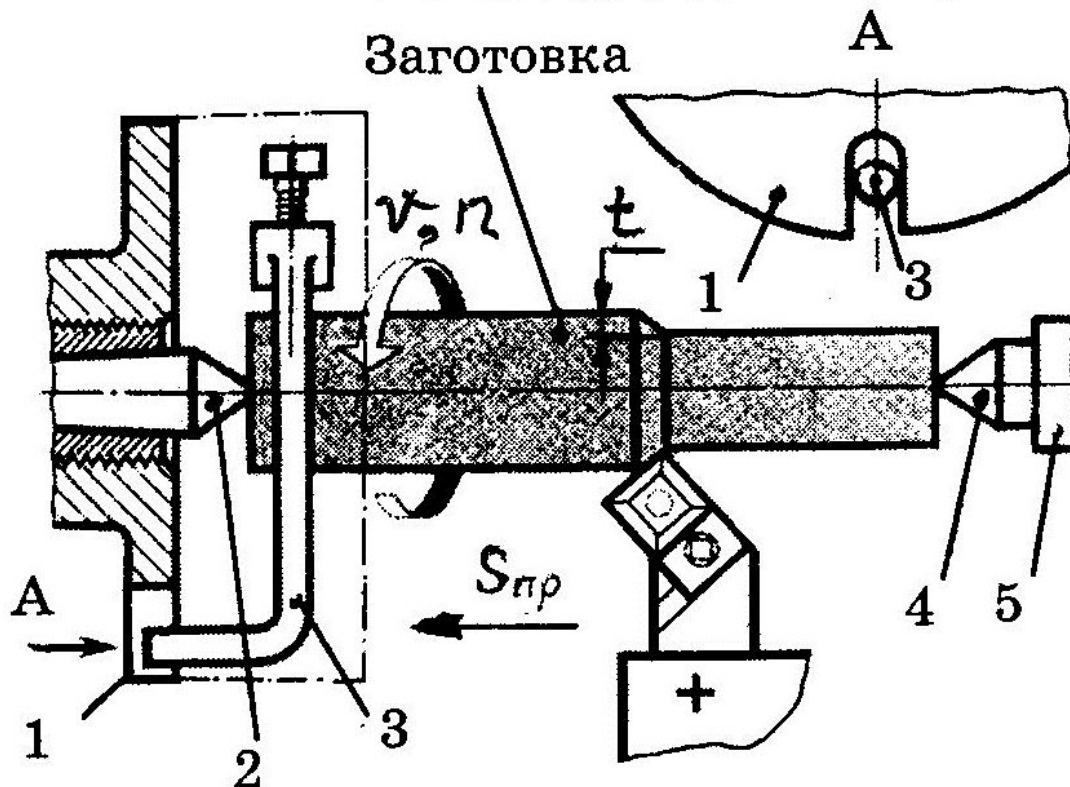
Обтачивание заготовки, установленной в центрах: 1 – планшайба (патрон с кожухом, указанным штрихпунктирной линией); 2 – центр передней бабки; 3 – поводок (хомутик); 4 – собственно центр задней бабки; 5 – корпус вращающегося центра; параметры режима –  $v$ ,  $n$ ,  $S_{пр}$ ,  $t$  соответственно скорость обработки, частота вращения заготовки, продольная подача, глубина резания.
